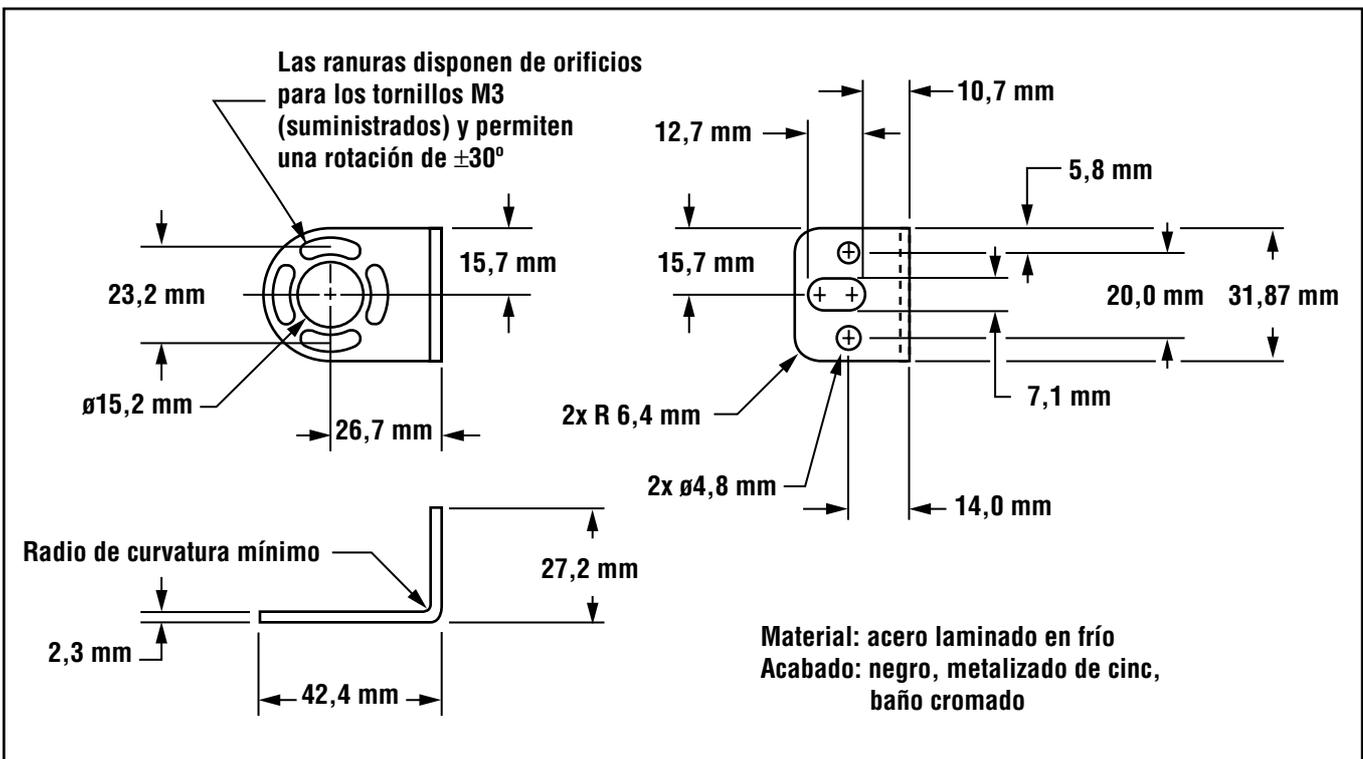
Dimensiones de las escuadras de Montaje de Emisor y Receptor
